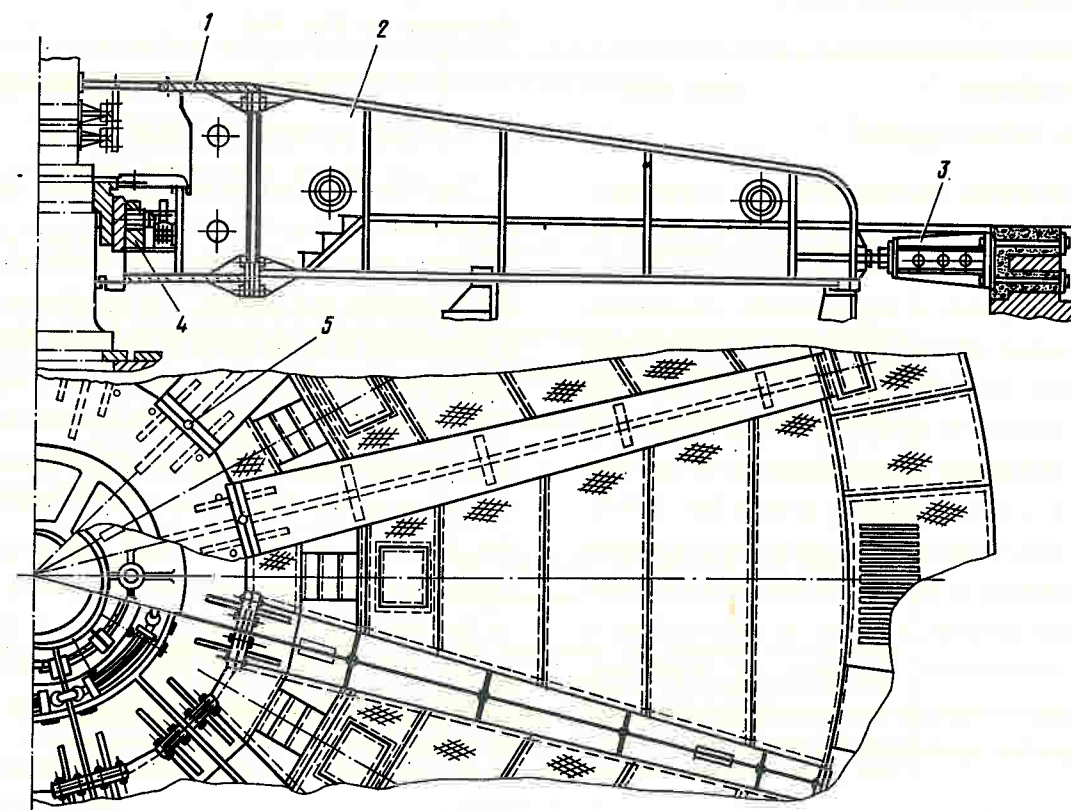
Верхняя крестовина лучевого типа: 1 — центральная часть; 2 — лапы; 3 — распорный домкрат; 4 — узел подшипника; 5 — штифт лапы
